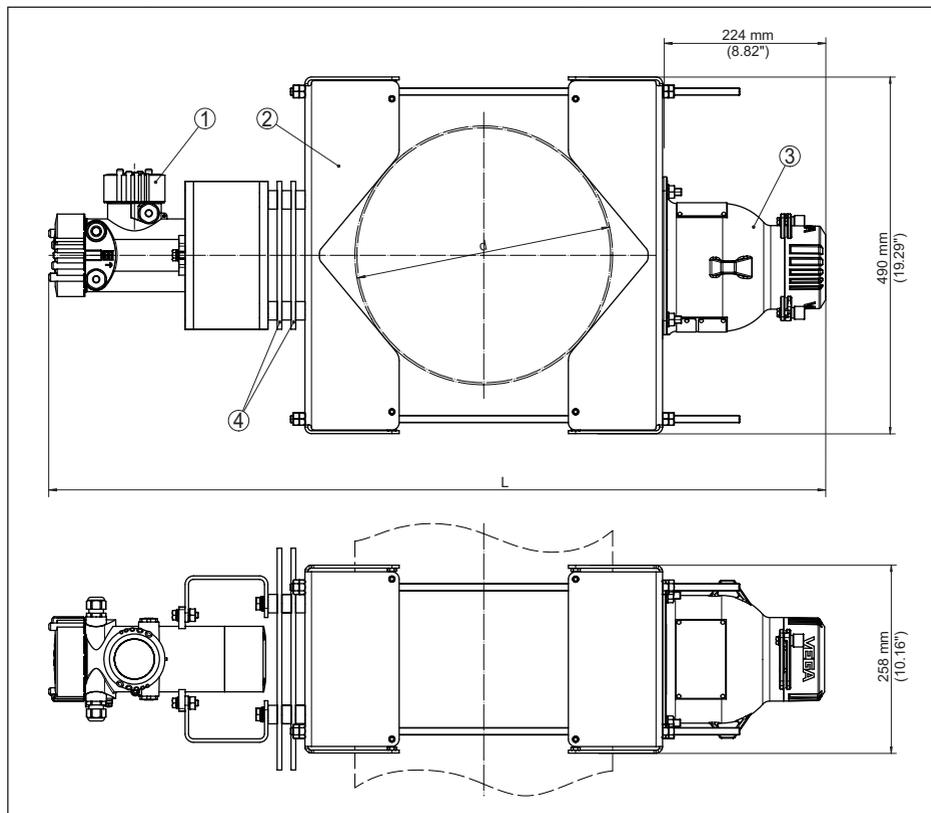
Dispositivo de fixação com sensor montado na horizontal e kit de proteção térmica (com VEGASOURCE 81, 82, 83)
